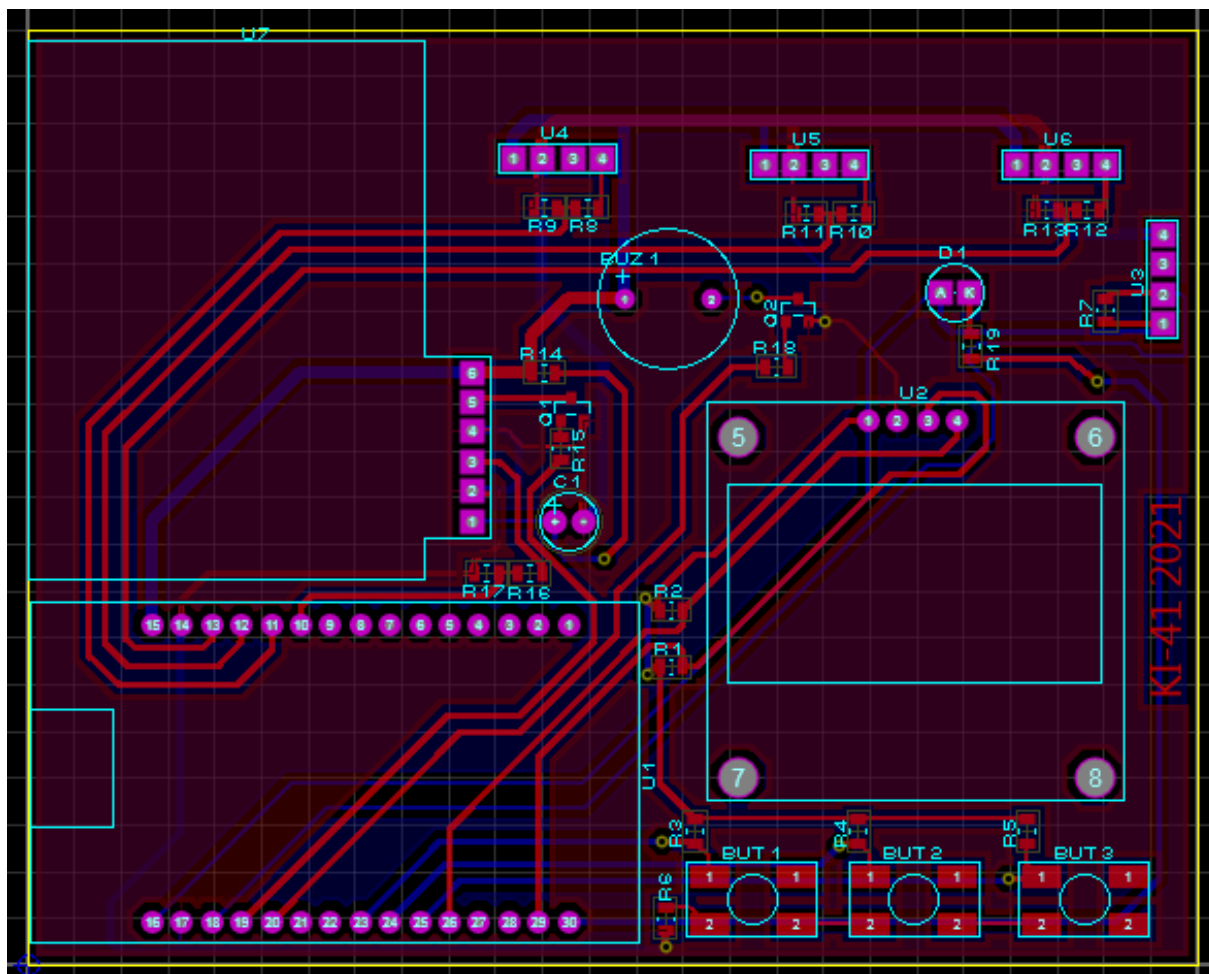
Вигляд друкованої плати розробленого пристрою
